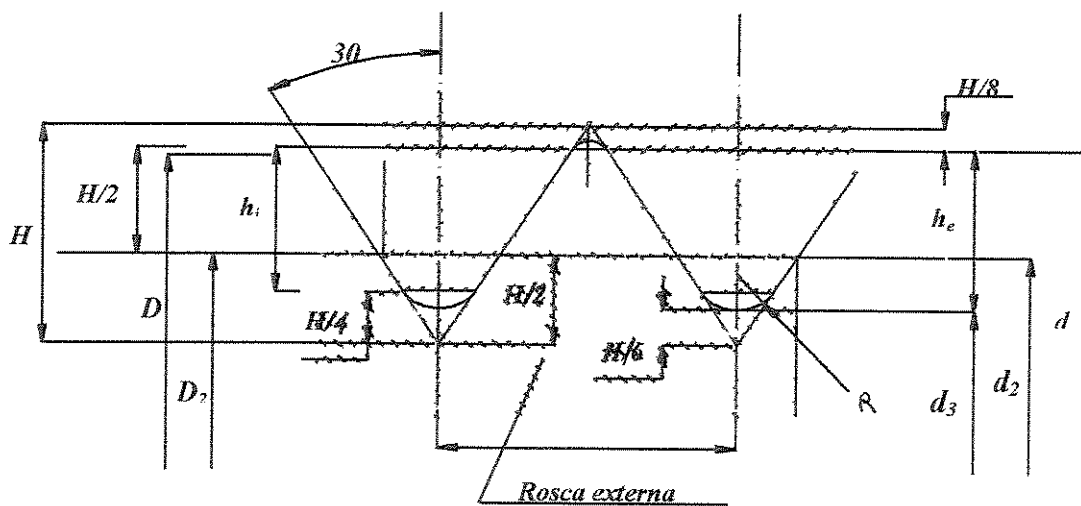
Perfil de projeto – Rosca métrica ISO – Dimensões NB97 – Norma Brasileira para desenho técnico
